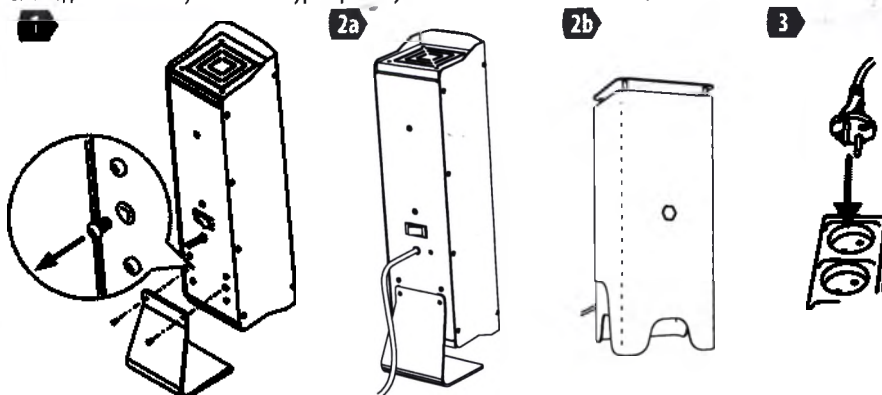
Сборка и установка очистителей воздуха ОВУ-01 и ОВУ-02
